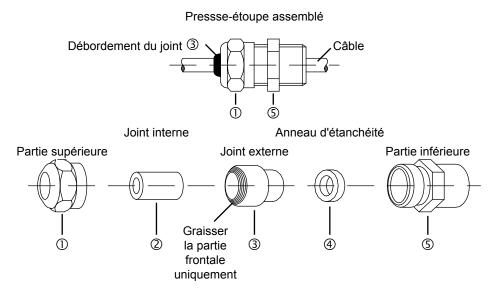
Presse-étoupe (vue d'ensemble et explosée)
